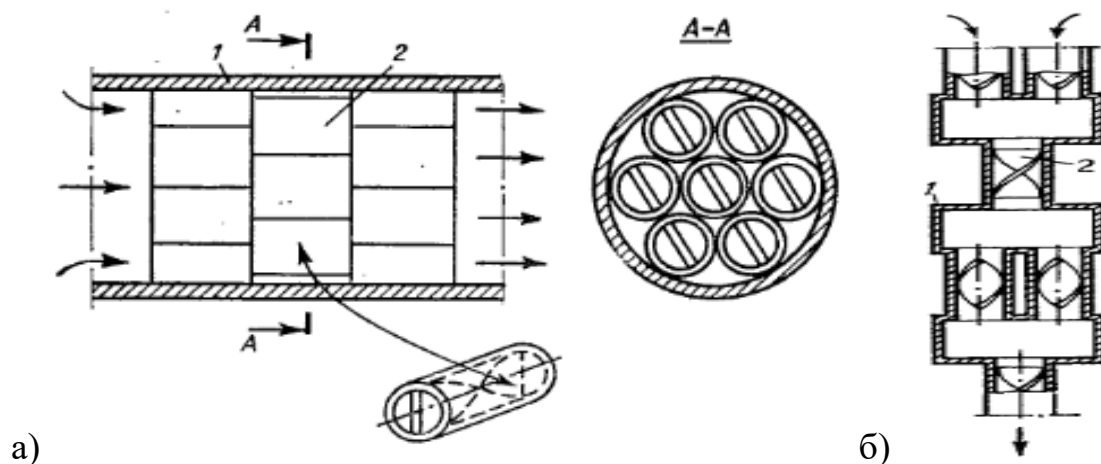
Конструкция смесителя с параллельным расположением винтовых элементов: а – пакетная установка; б – чередование параллельной и последовательной установки; 1 – корпус смесителя; 2 – смесительные элементы
